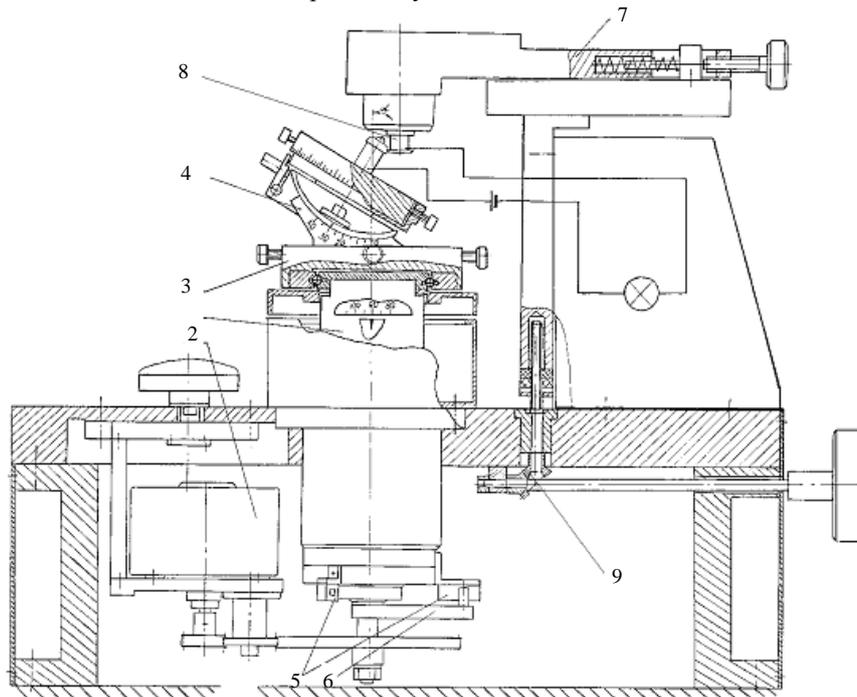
Установка для формирования профиля: 1 – шпиндель; 2 – двигатель; 3 – каретка; 4 – угловая оправка для опоры; 5 – переключатель; 6 – флажок; 7 – узел притира; 8 – притир; 9 – коническая передача
